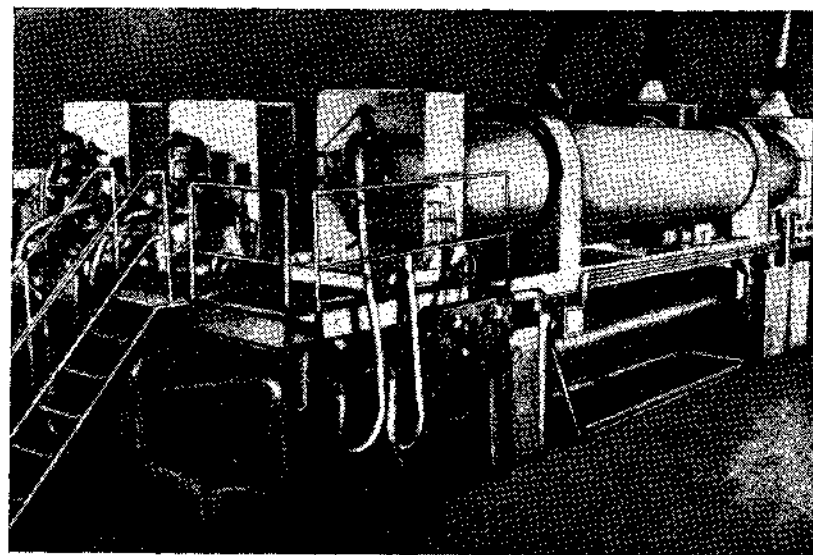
Общий вид барабанной печи прямого нагрева для обжига ферритовой шихты
